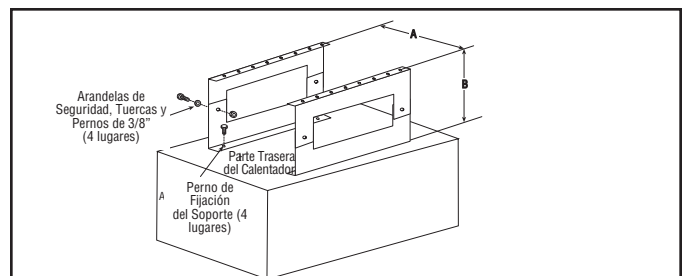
Instalación del Calentador sobre el Soporte de Montaje
